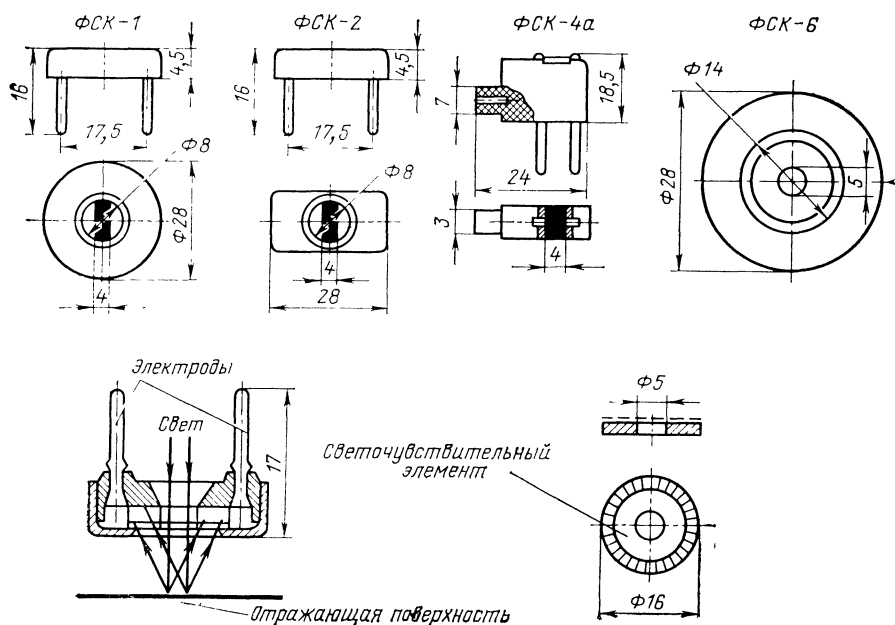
Фоторезисторы в пластмассовых корпусах.
